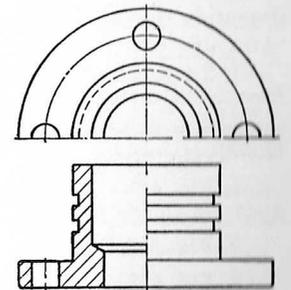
Planta em meia vista e uma meia vista meio corte
